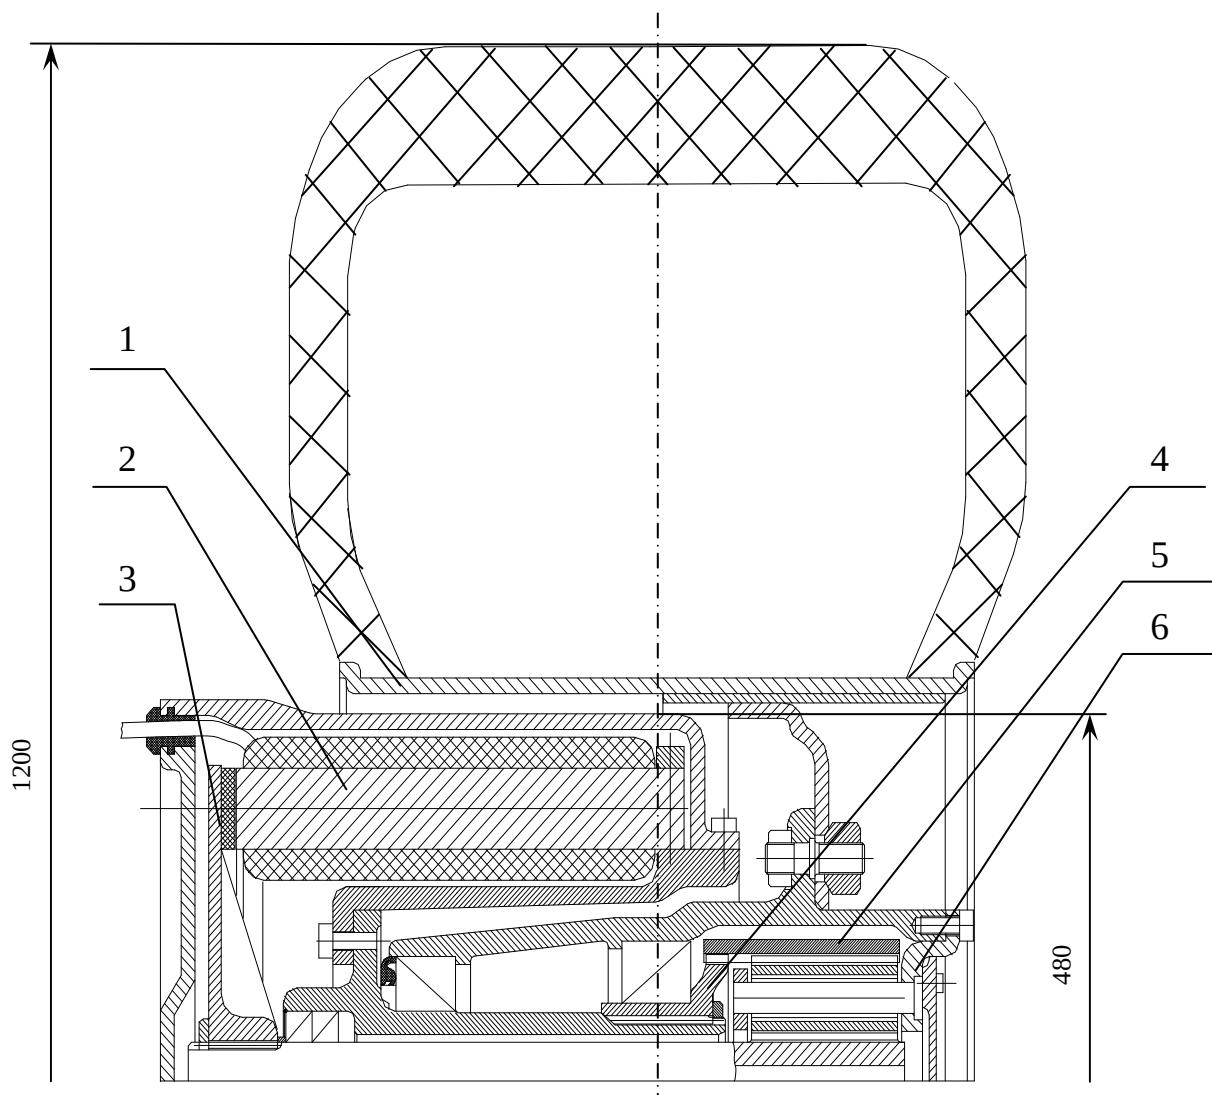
Мотор-колесо с однорядным редуктором:
